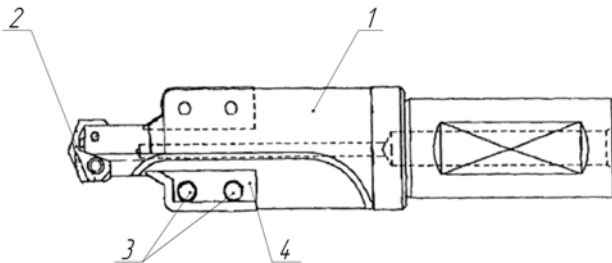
Свердло-зенківка фірми Hayes Lemmerz International
